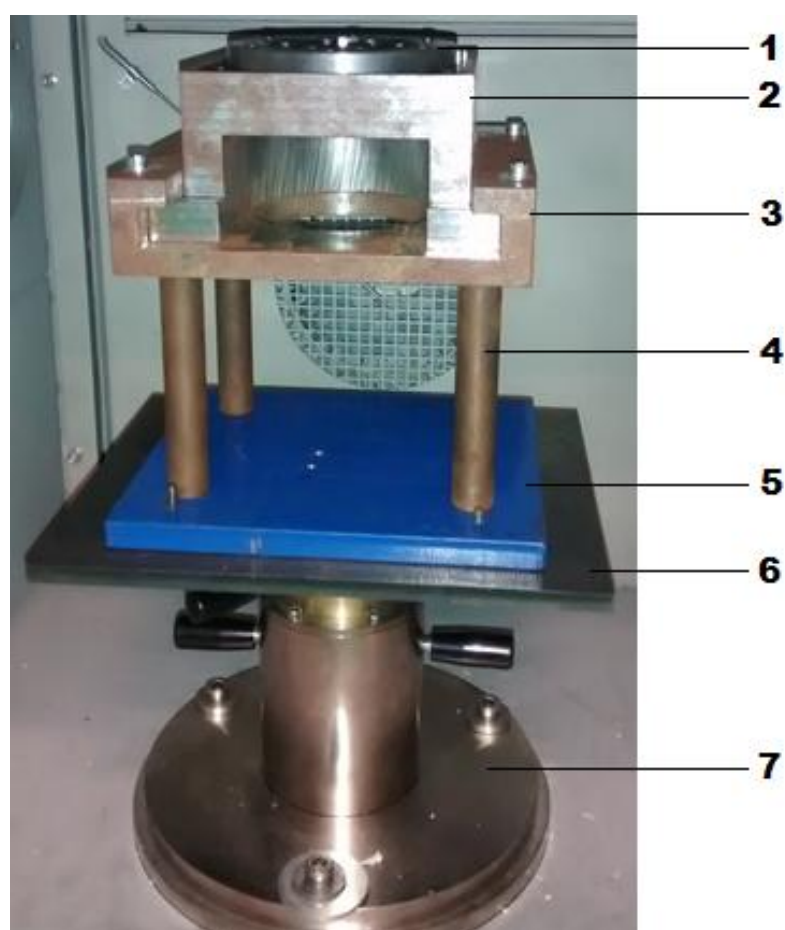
Partes del útil completo: 1.-Útil probetas circulares. 2.-Pieza 3 útil para probetas cuadradas. 3.-Piezas 1 y 2 útil probetas cuadradas. 4.-Soporte vertical para elevar el útil. 5.- Placa de soporte 1. 6.-Placa de soporte 2. 7.-Base de fijación a la torre.
